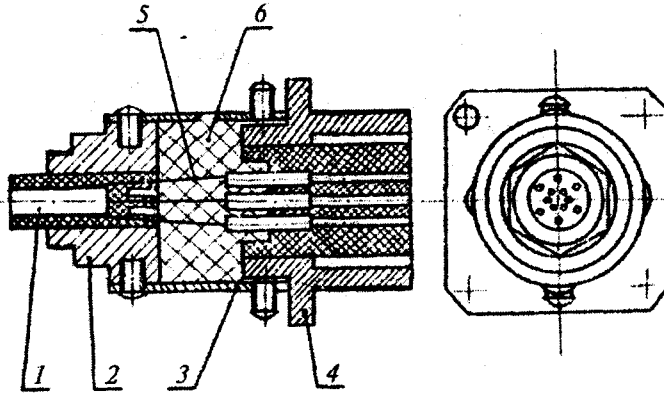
Датчик для стендовых испытаний: 1 — образец; 2 — держатель; 3 — соединительная втулка; 4 — разъем; 5 — термоэлектрод; 6 — эпоксидная смола
